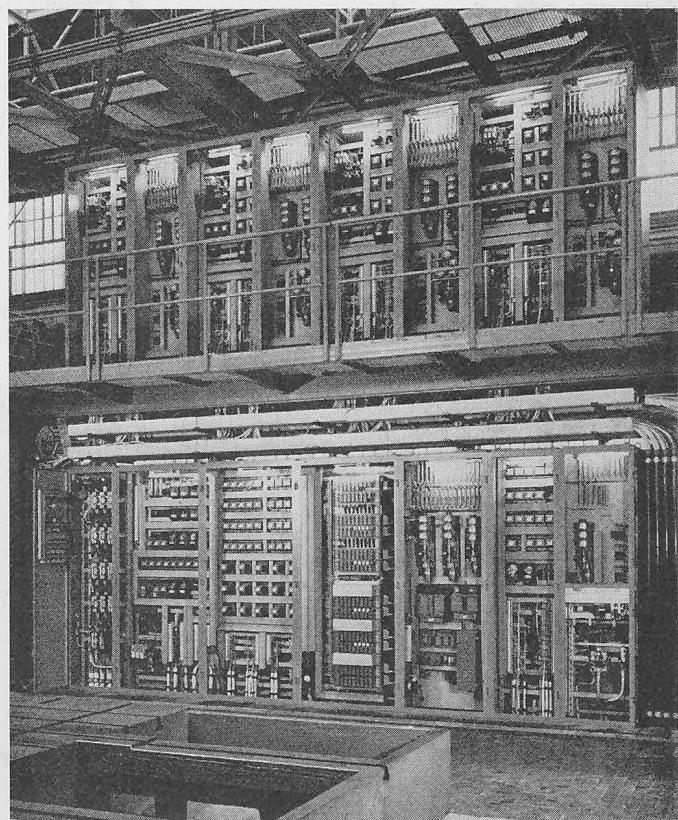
Hauptschalschränke für das Schiess-Hobel- und Fräswerk
